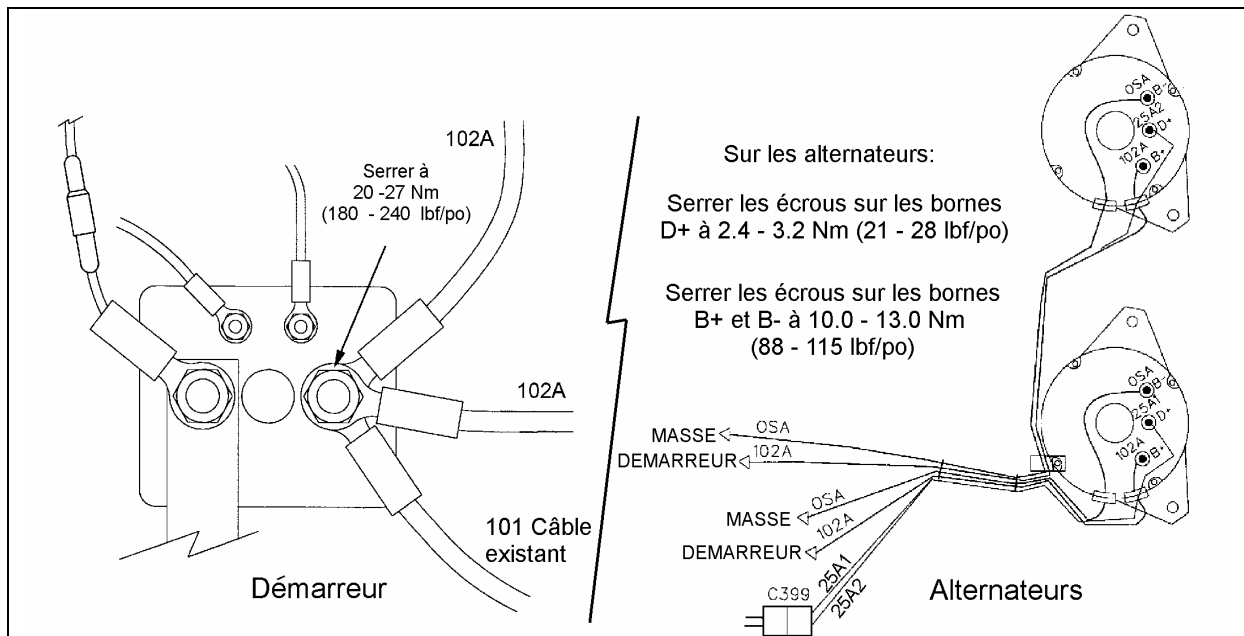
INSTALLATION DES CABLES SUR L'ALTERNATEUR ET SUR LE DEMARREUR
